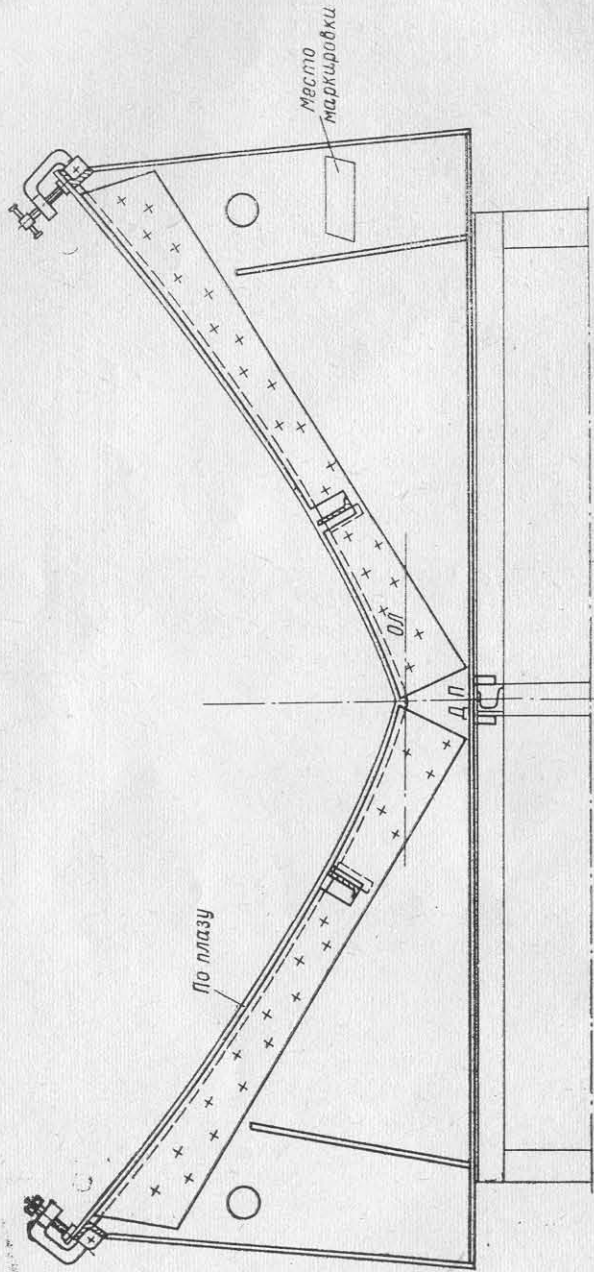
Постель для сборки и сварки днищевой секции.
